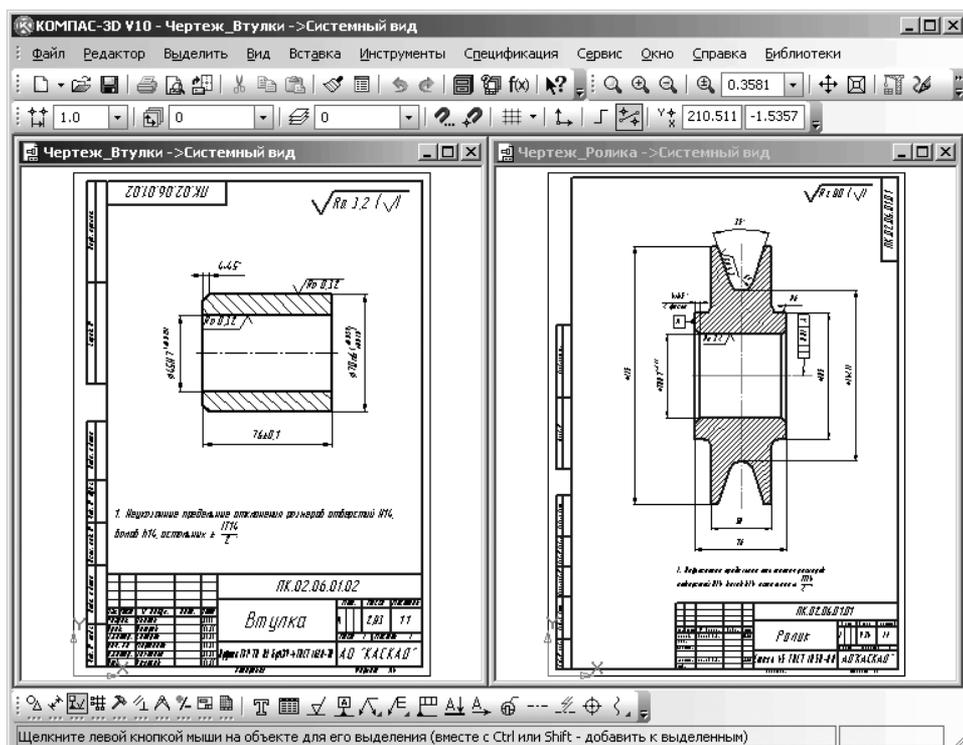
Представление деталей перед созданием сборочного чертежа Ролик_Втулка
